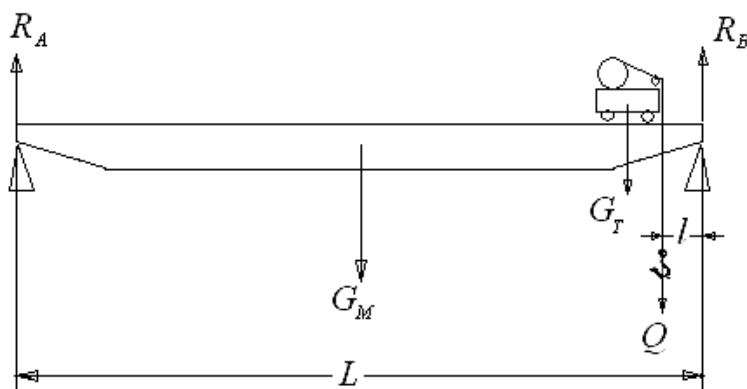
схема к определению нагрузок на концевые балки моста крана
